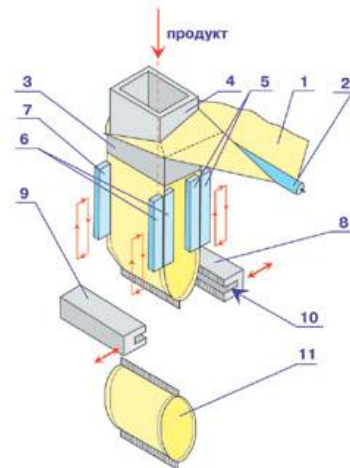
Компонування машини з губками зварювання бокових швів: 1 – плівка; 2 – механізм натягу плівки; 3 – формувальний ворот; 4 – рукавотворювач; 5, 6, 7 – губки зварювання бічних швів; 8, 9, 10 – губки поперечного зварювання; 10 – відрізний механізм; 11 – готовий пакет
